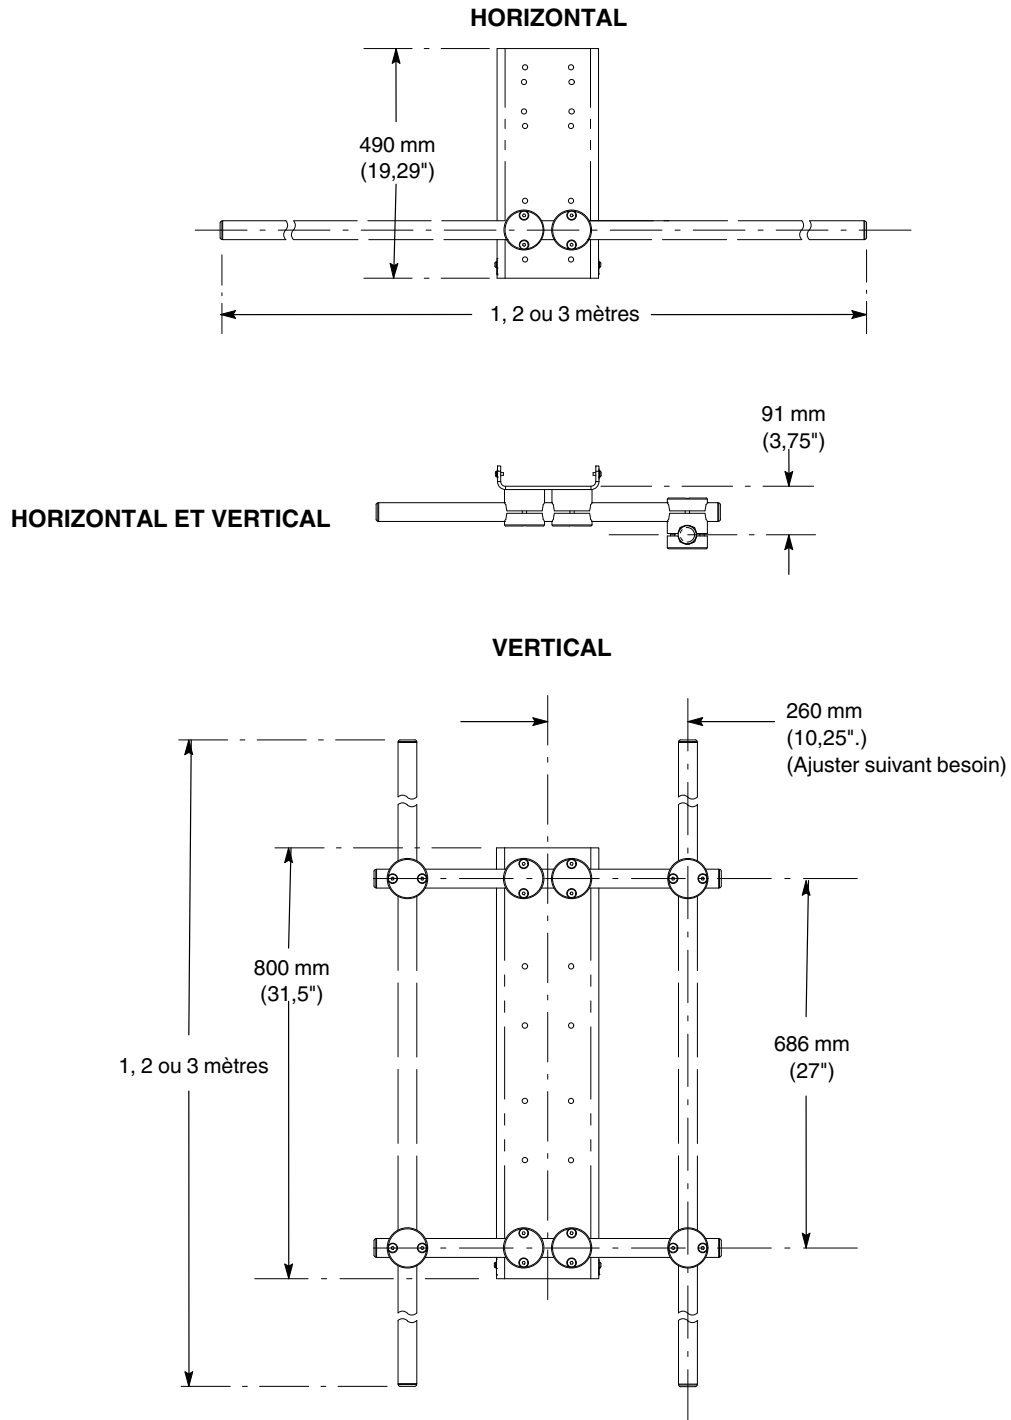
Dimensions des supports de pistolet simple horizontaux et verticaux
